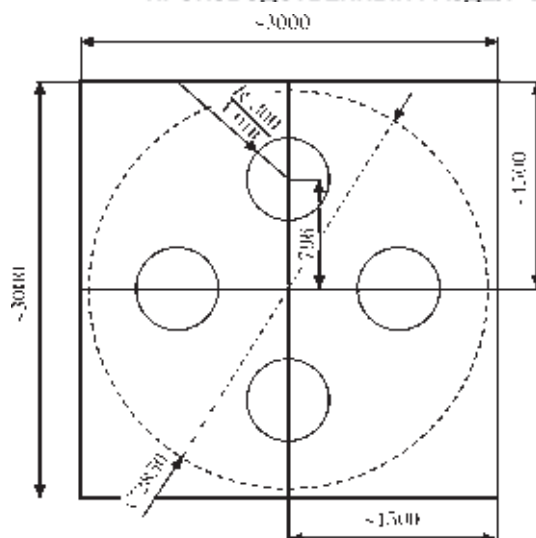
Эскиз конструкции плиты из магниевого сплава МА2 (штрихпунктирная — диаметр заготовки, вырезаемой после сварки)
